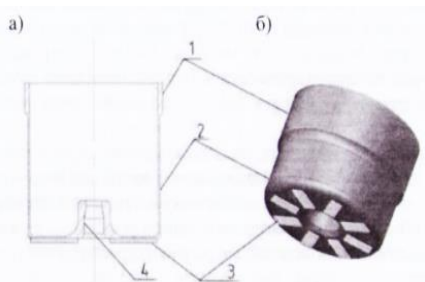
Разрез (а) и общий вид (б) цилиндрического резонатора:
